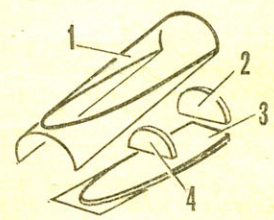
Изготовление хвостового поплавка: 1 — корпус поплавок, 2 — кормовой шпангоут, 3 — подошва, 4 — вспомогательный шпангоут.
